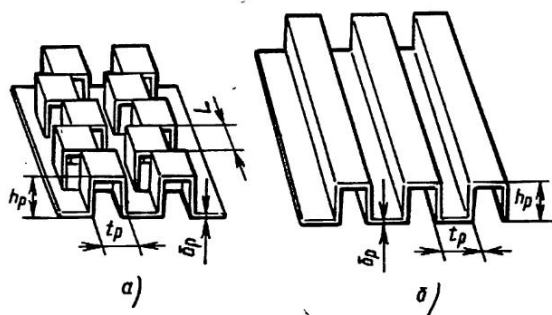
Насадка пластинчато-ребристой поверхности:
